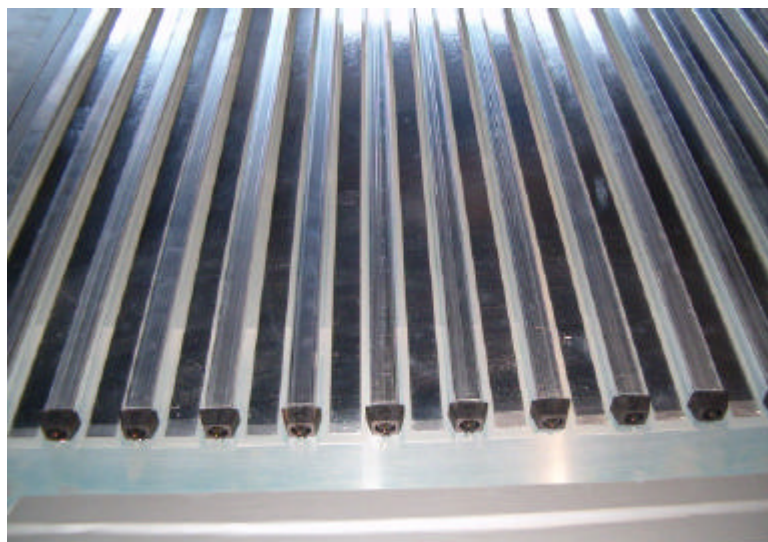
Vigas y posicionadores fijos adheridos a una plancha
